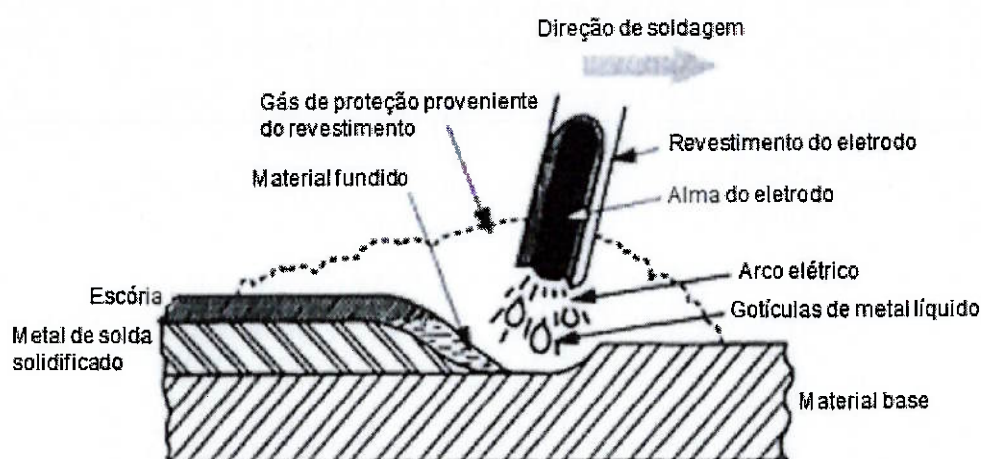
Esquema de soldagem por eletrodo revestido [6].
